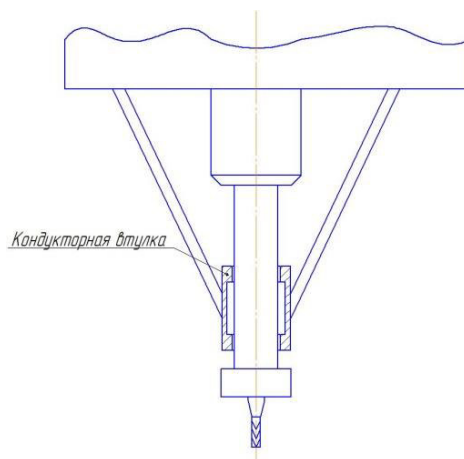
Схема устройства удлинителя с кондукторной втулкой
